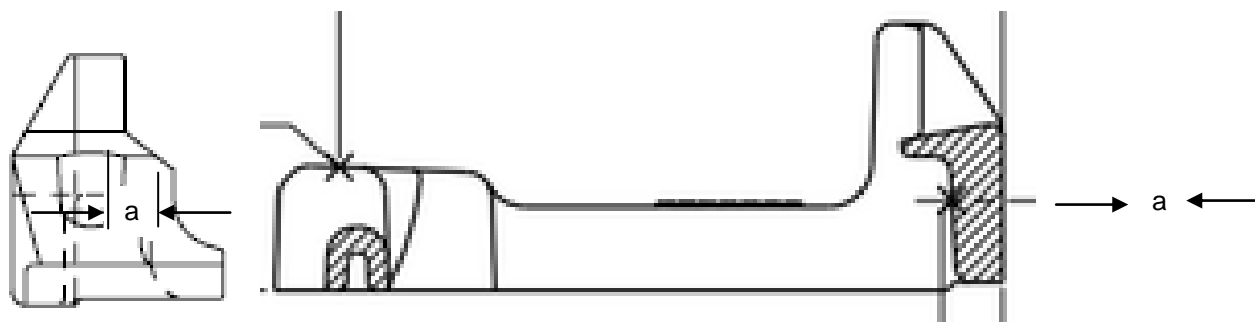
Поперечный разрез боковых изоляторов для крепления Fastclip (Pandrol)
